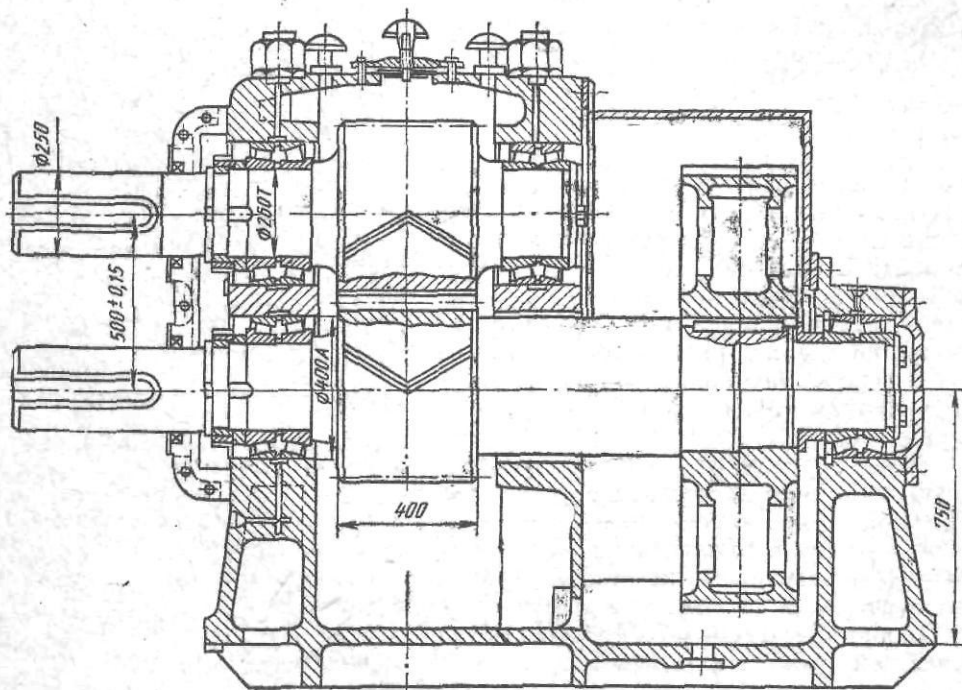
Комбинированная шестеренная клетка-редуктор четырехвалковой клетки дрессировочного стана 2500 конструкции ВНИИметмаша НКМЗ
